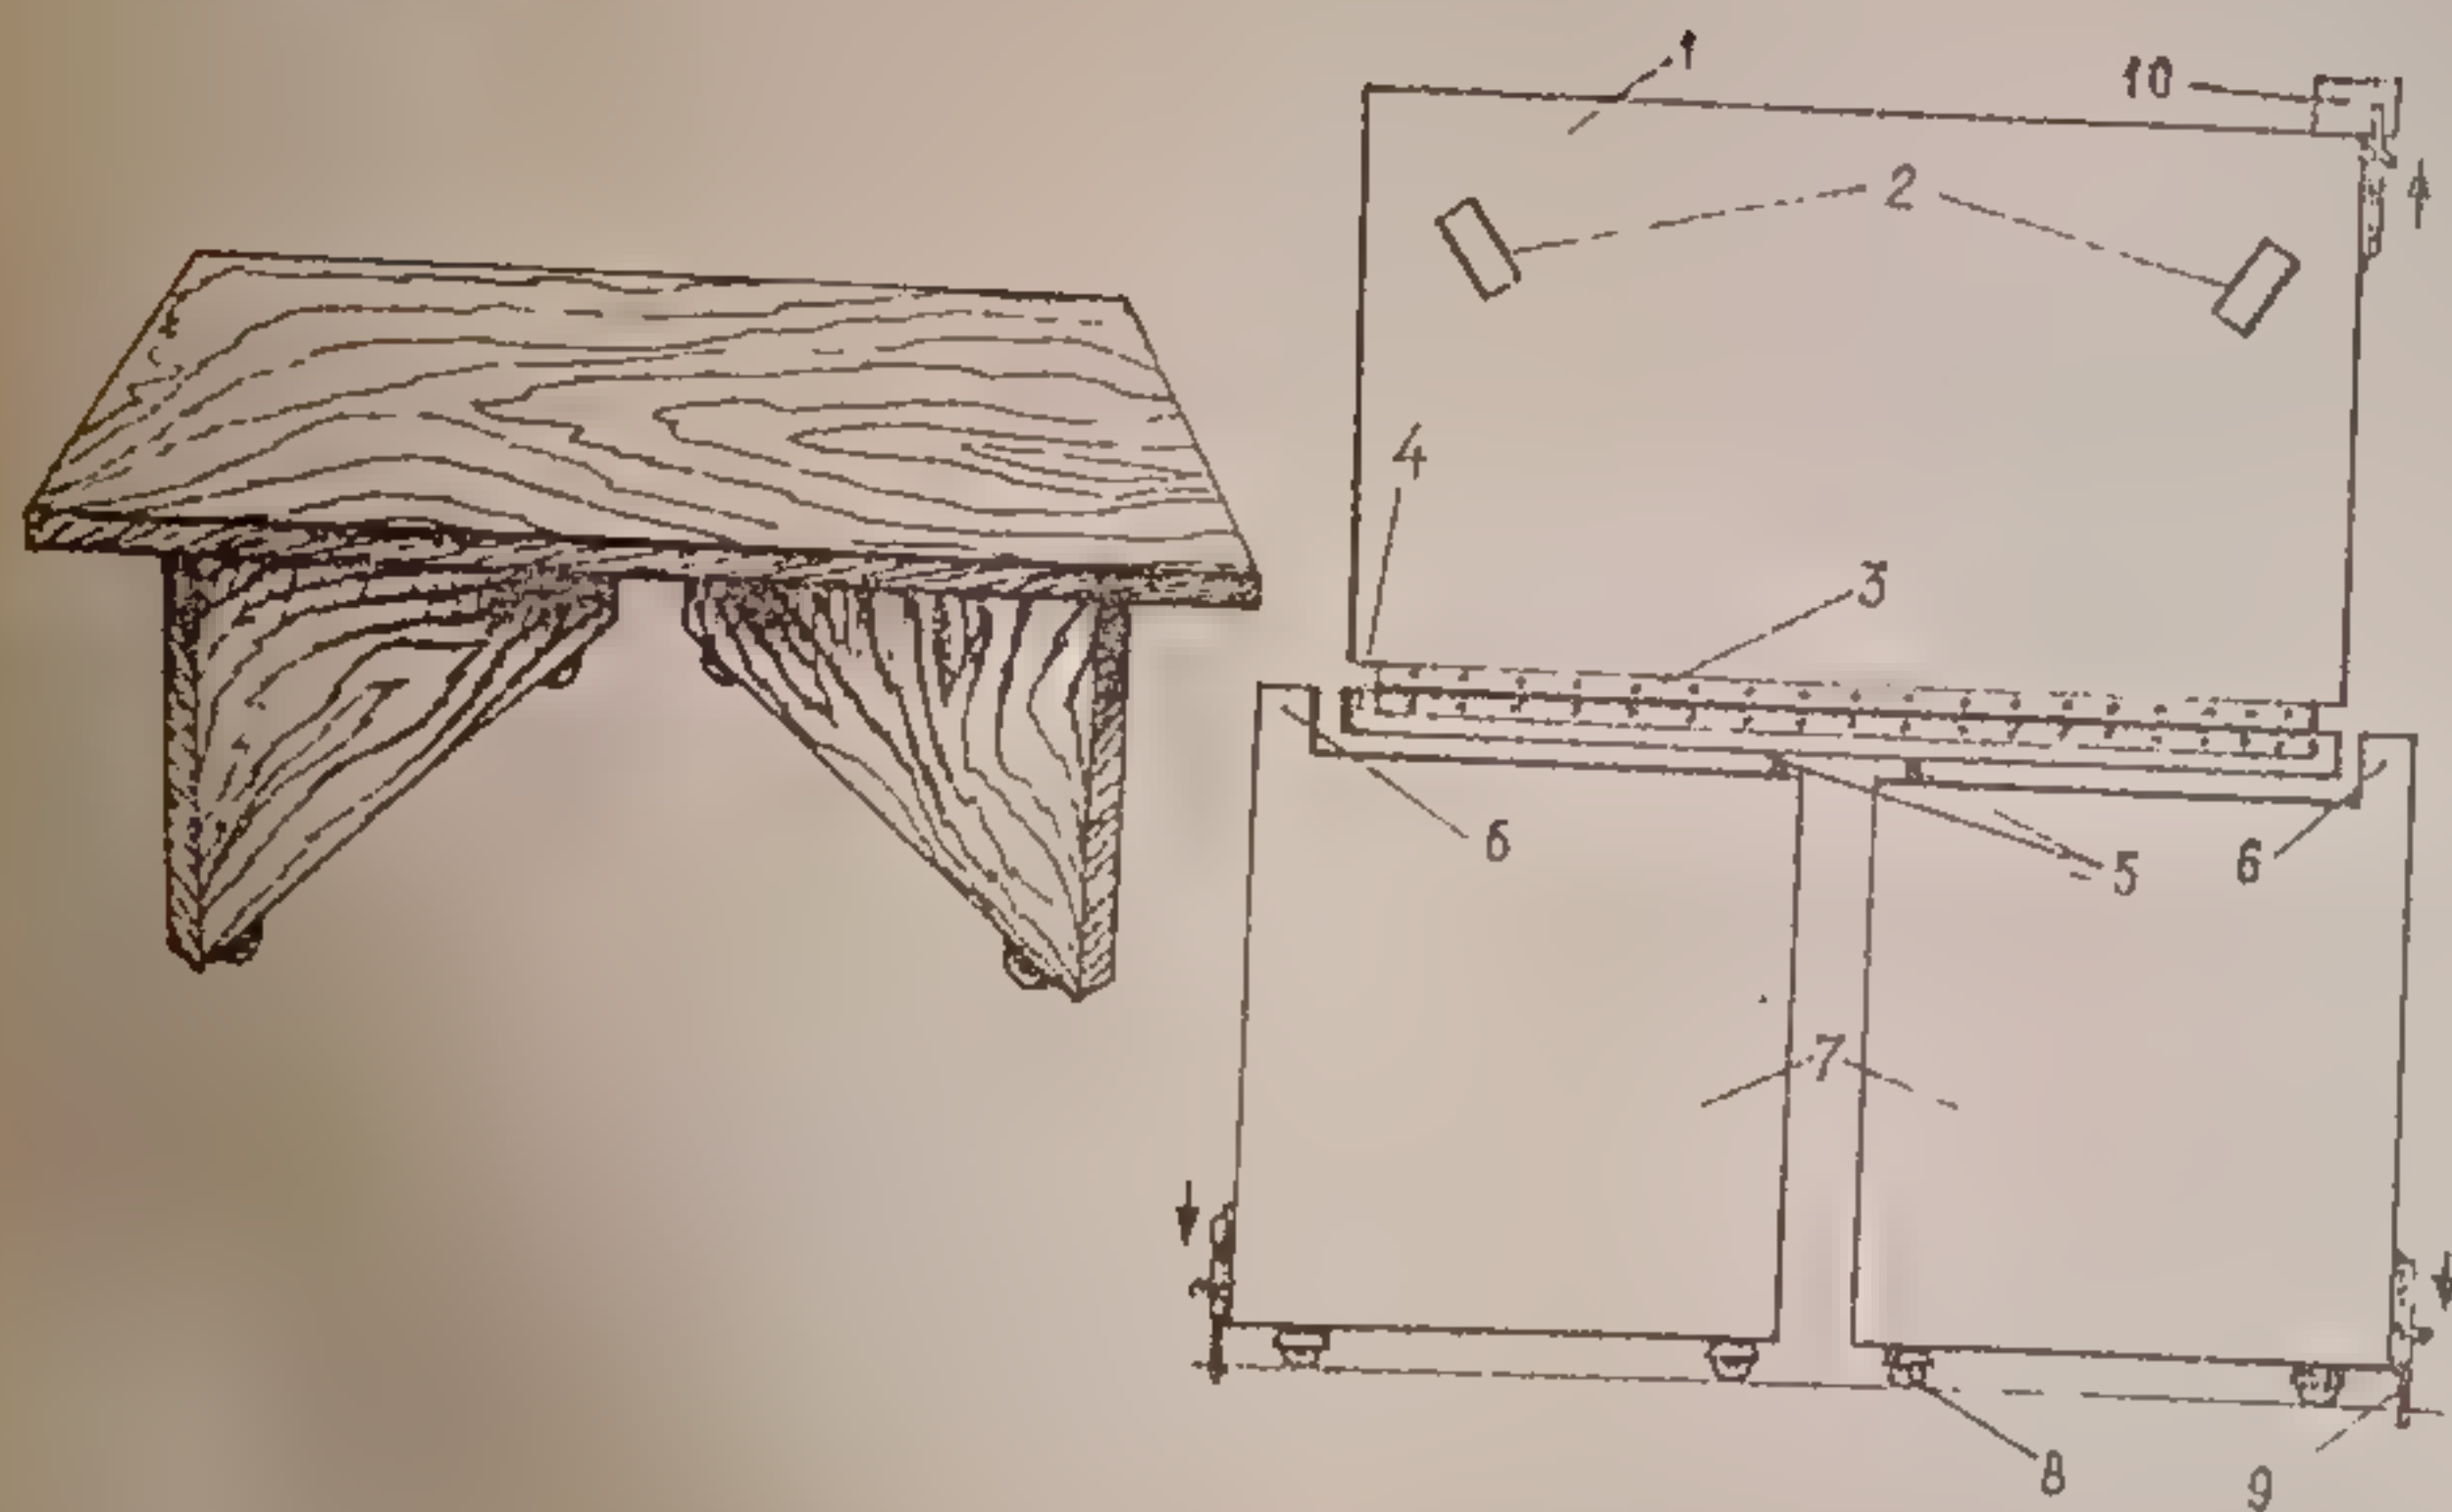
Составно-накладной стол: 1 — столешница; 2 — глухие отверстия снизу крышки стола; 3 — рояльная петля; 4 — опорный брусок; 5 — металлические штыри; 6 — бобышки боковин; 7 — опорные боковины; 8 — колесики [шарикоподшипники]; 9 — шпингалеты мебельные; 10 — кубик деревянный с отверстием для захода штифта шпингалета
